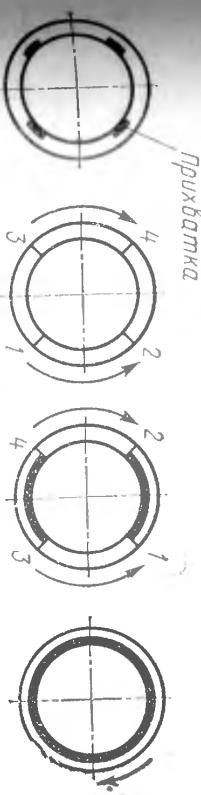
Порядок сварки поворотных стыков трубопроводов
